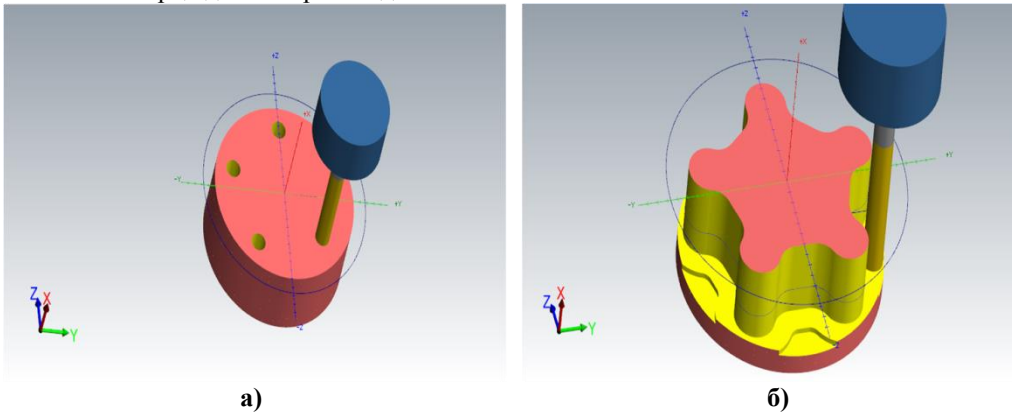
3D симуляция фрезерной операции: а – сверление пяти отверстий на торце, б – контурное наружное фрезерование.
